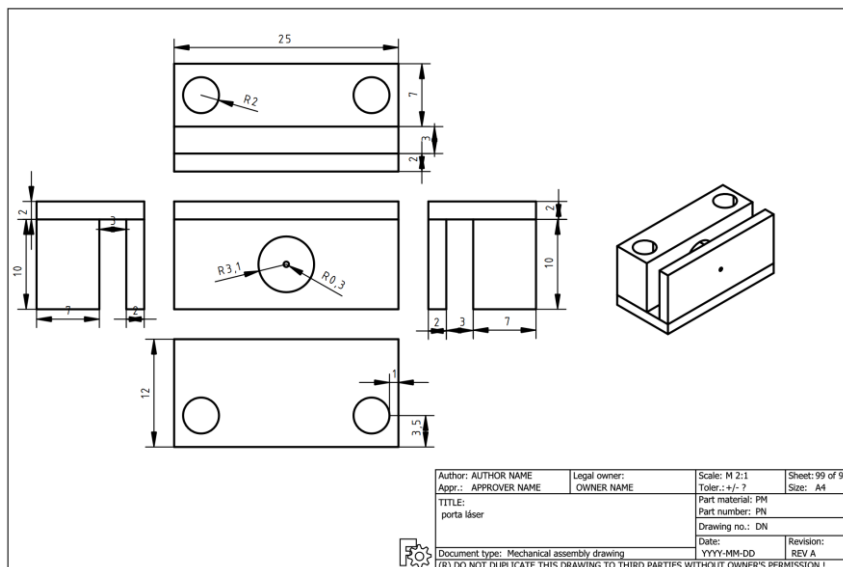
Dimensiones del zócalo sobre el que va insertado el láser
